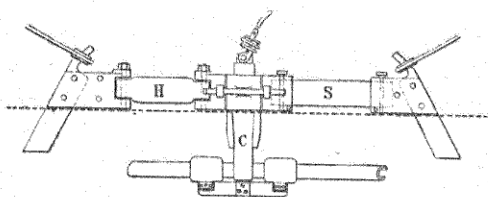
Ensemble de la prise de courant du caniveau de Blackpool.
